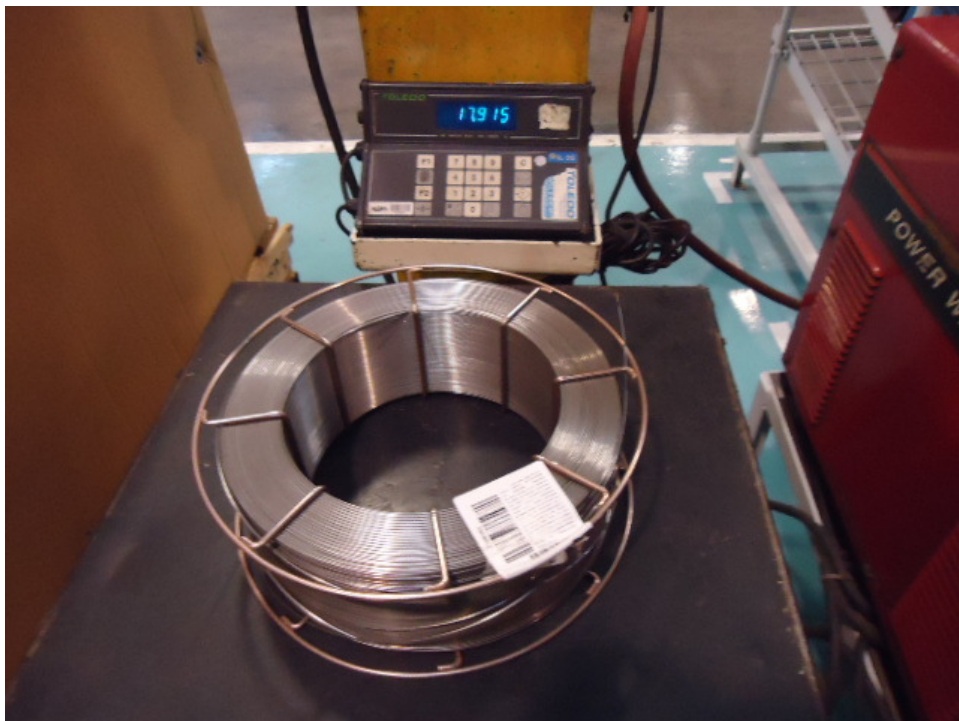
Arame após a soldagem com mistura 15% CO₂
